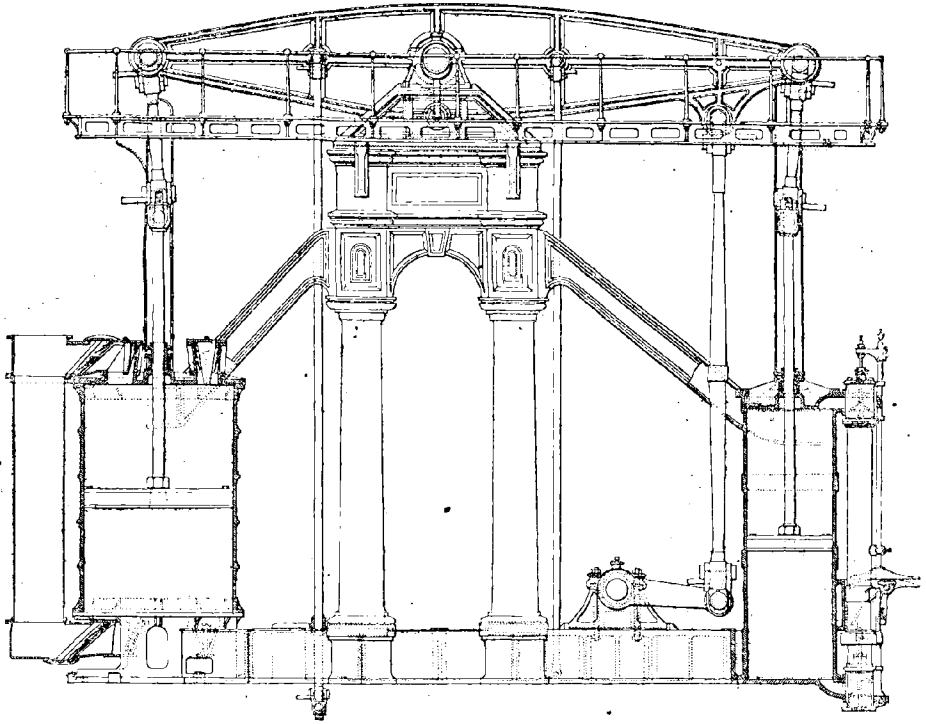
Machine soufflante à balancier de Rumpf (coupe verticale).
